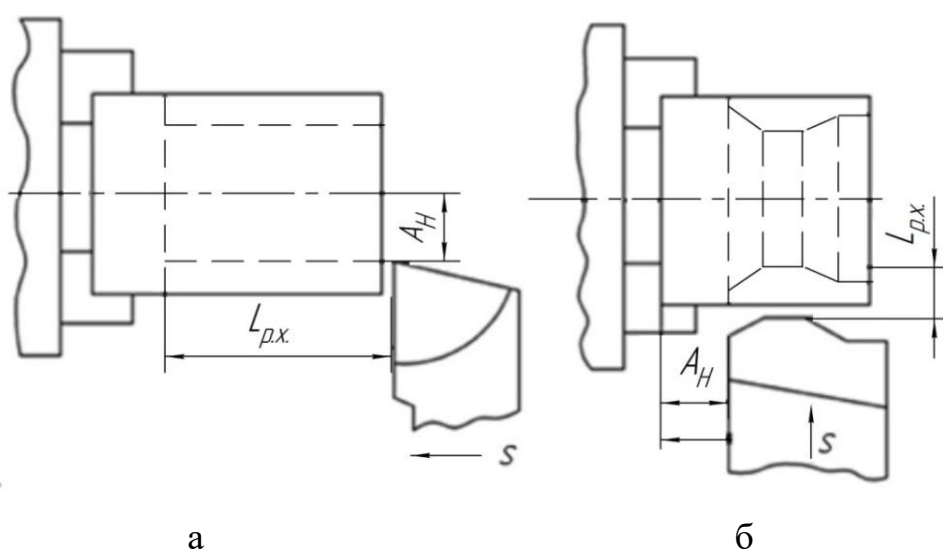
Схема размерной настройки при токарной обработке:
